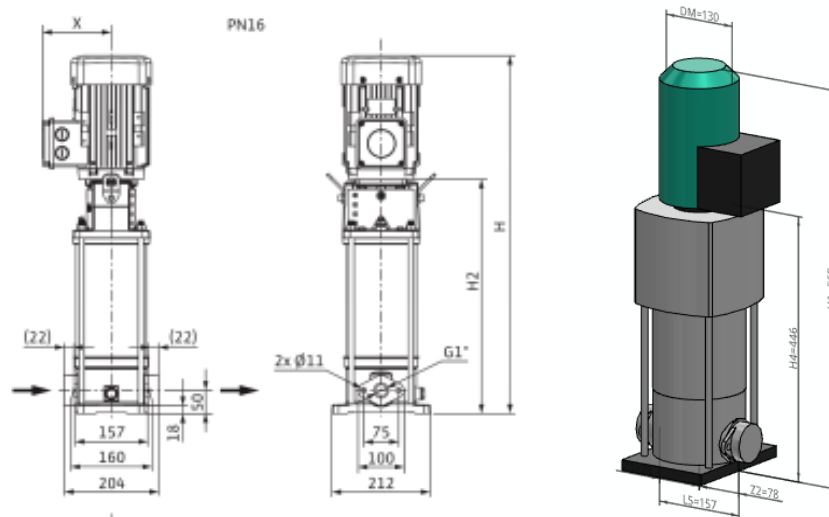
Dimensiones bomba Wilo HELIX V205-1
